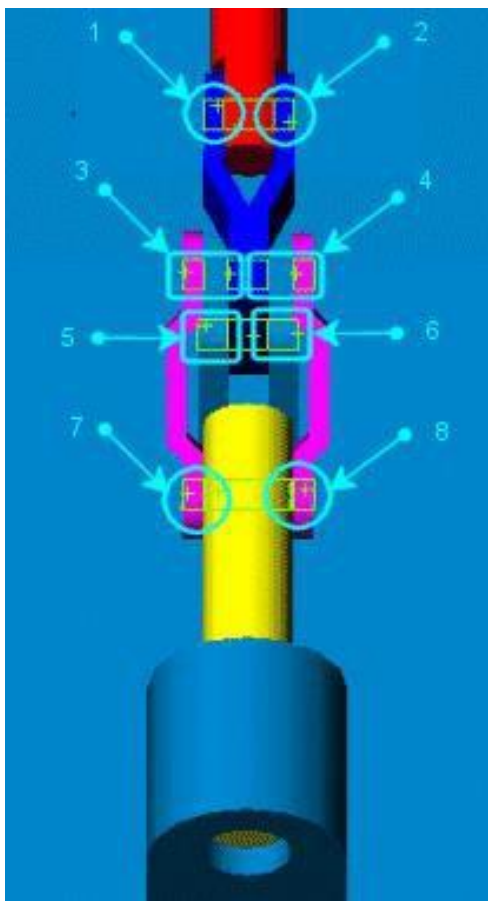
Соединения «шпилька» исполнительного механизма
